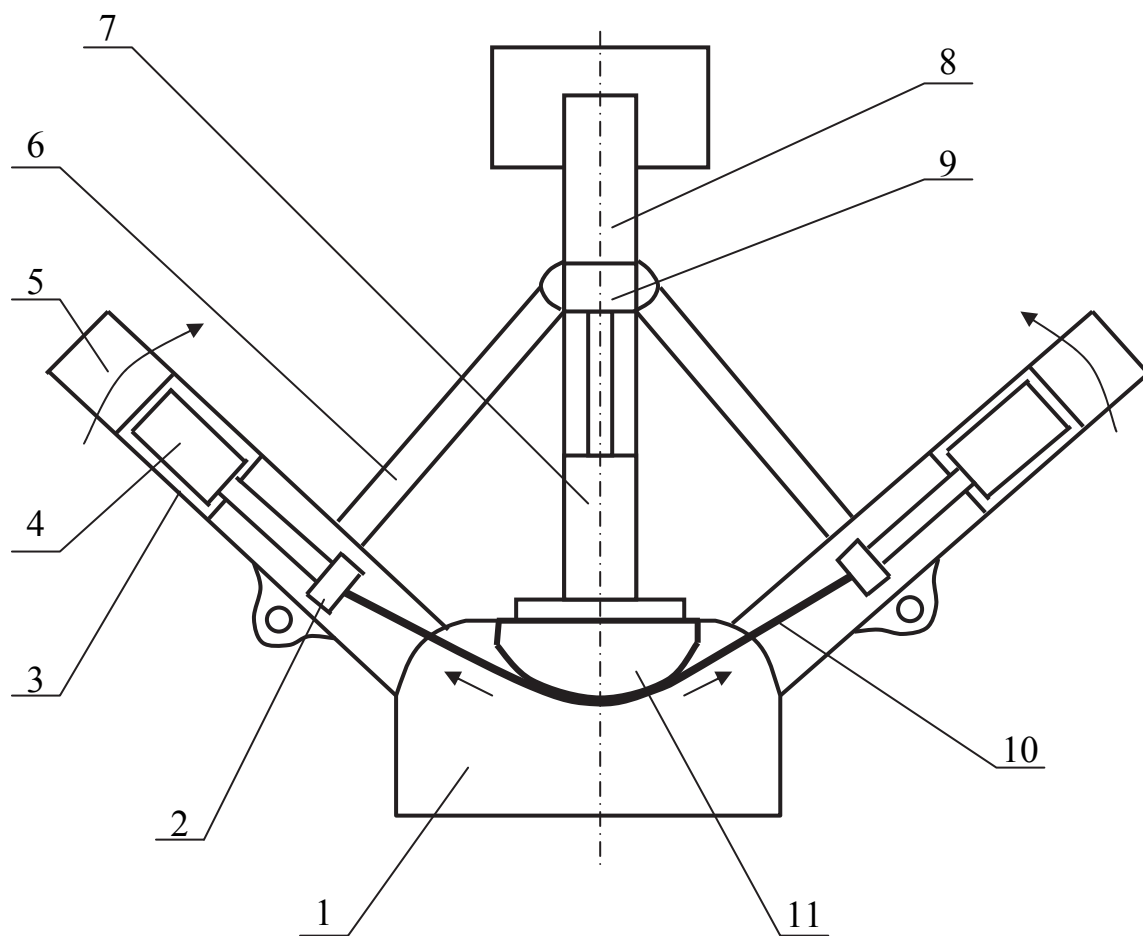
Основные элементы конструкции и схема изготовления детали на станке ПГР
